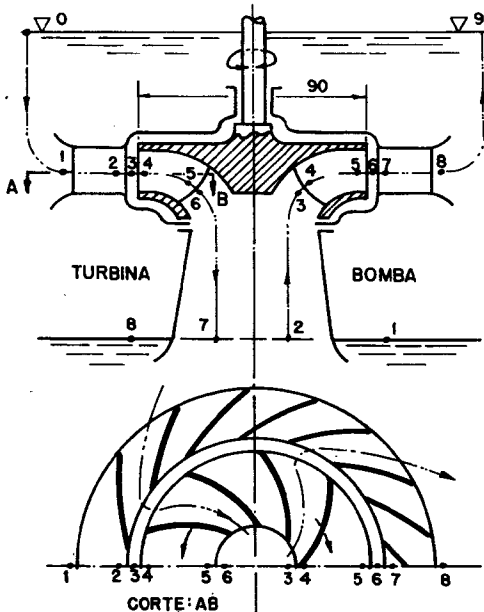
Convenções para turbinas e bombas hidráulicas.
